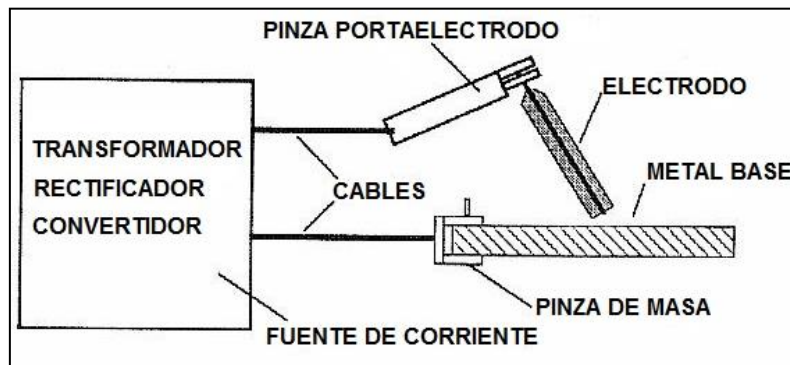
Equipo de soldadura tomado de <https://ingemecanica.com/tutorialsemanal/tutorialn45.html>
